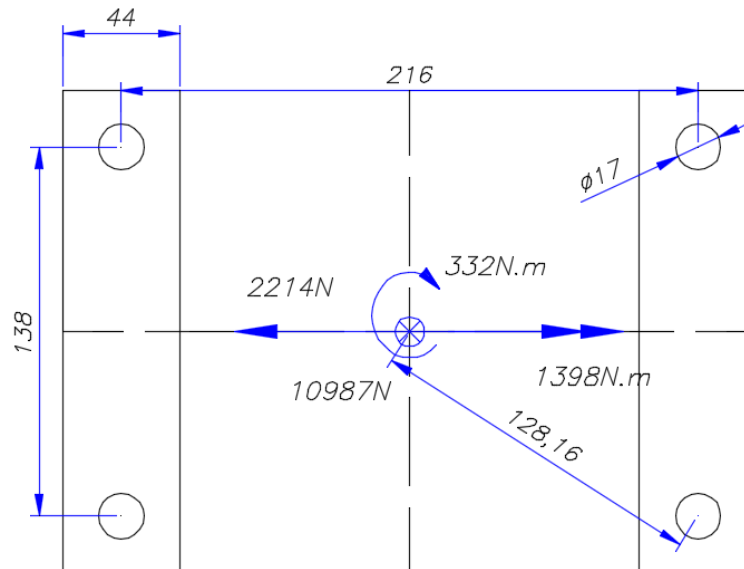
Dimensiones de unión atornillada de reductor para tornillos M16.
